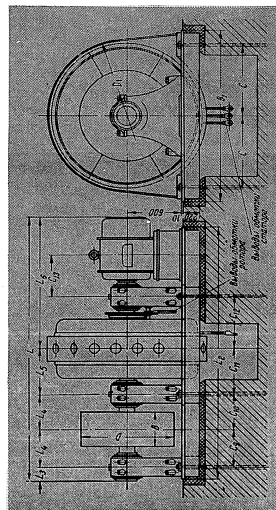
Размеры и вес спиральных машин на трех стоевых подшипниках со шлицом для ременной или газоройной передачи
